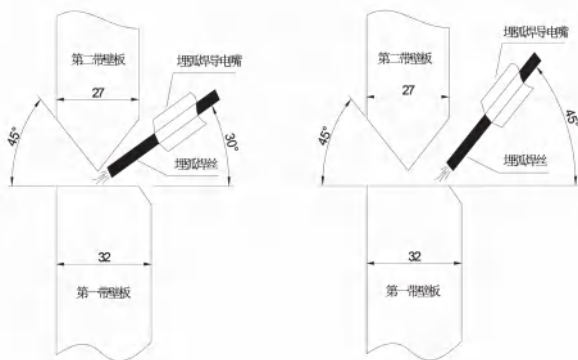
储罐 B1 环焊缝焊接时焊枪示意图
